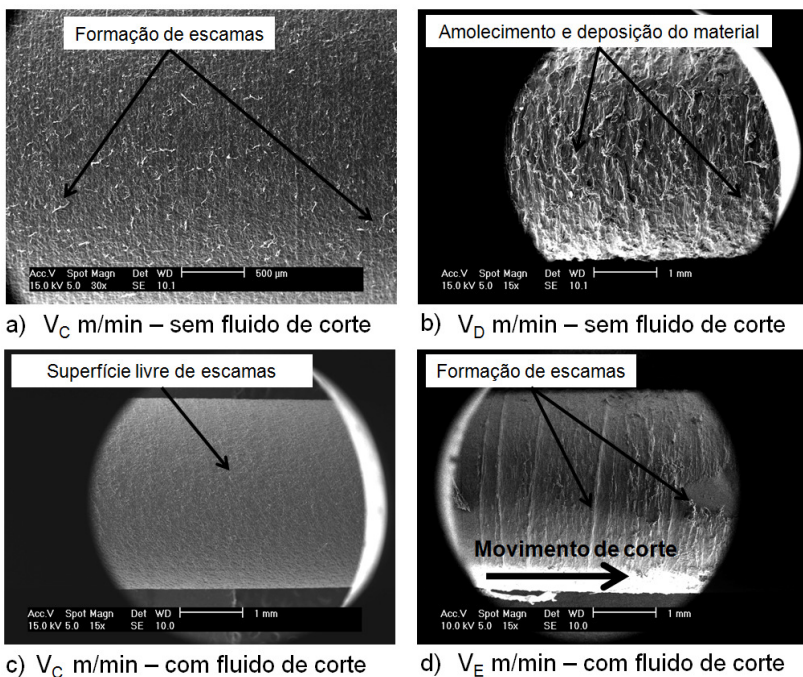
Imagens MEV das superfícies obtidas nos diferentes ensaios de usinagem.
